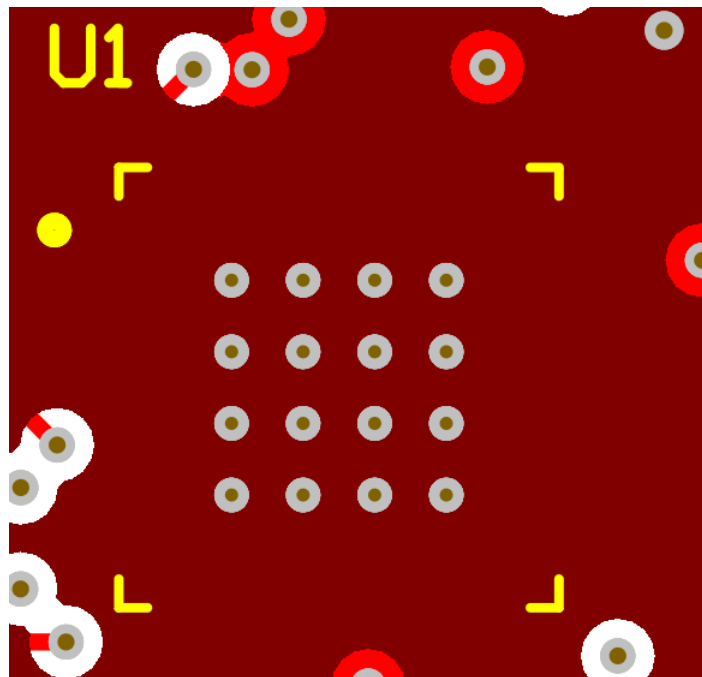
CDCDB800 的 PCB 布局示例，GND 层
